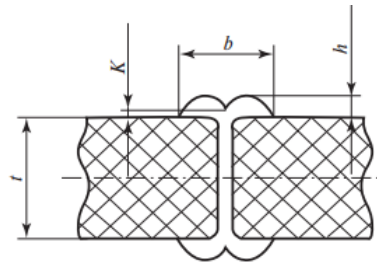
Основные геометрические размеры соединения встык труб из полиэтилена: t – толщина стенки трубы; b – ширина шва сварного соединения; h – высота шва сварного соединения; K – глубина впадины между валиками грата
